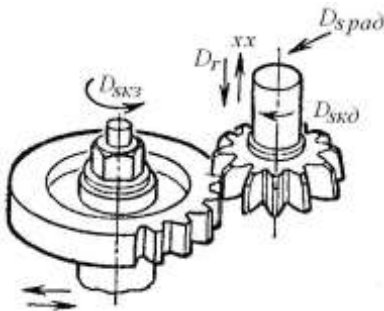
Схема нарізування зубців зубчастих коліс довбалами.
